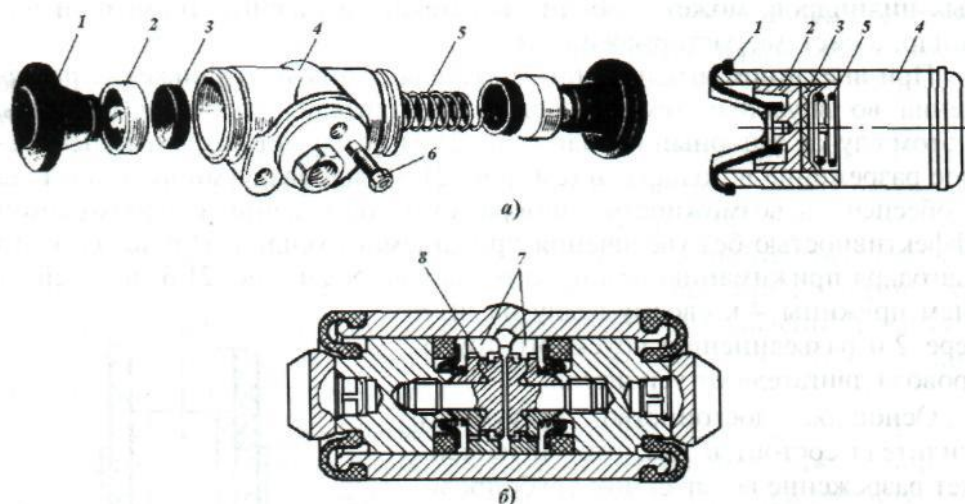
Колёсные цилиндры: а — колёсный цилиндр автомобиля ГАЗ-66-11; б — колёсный цилиндр заднего колеса легкового автомобиля
